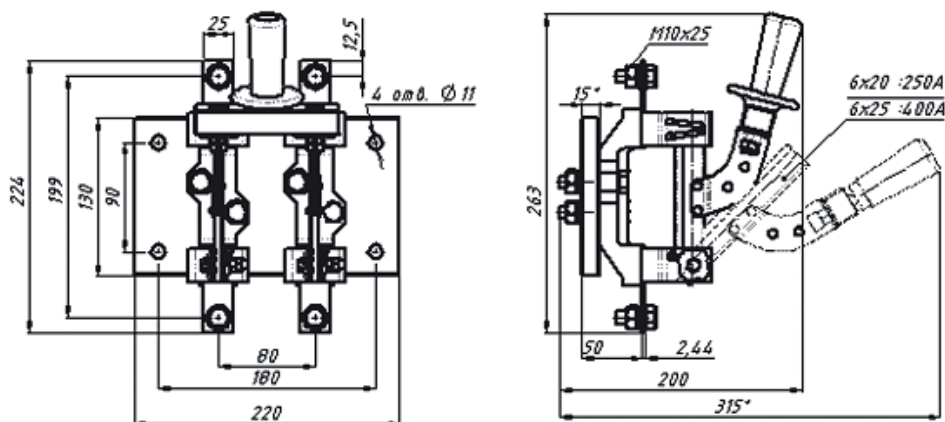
Разъединитель РЕ19-35(37)-31110-00 УХЛЗ трехполюсный с центральной рукояткой
